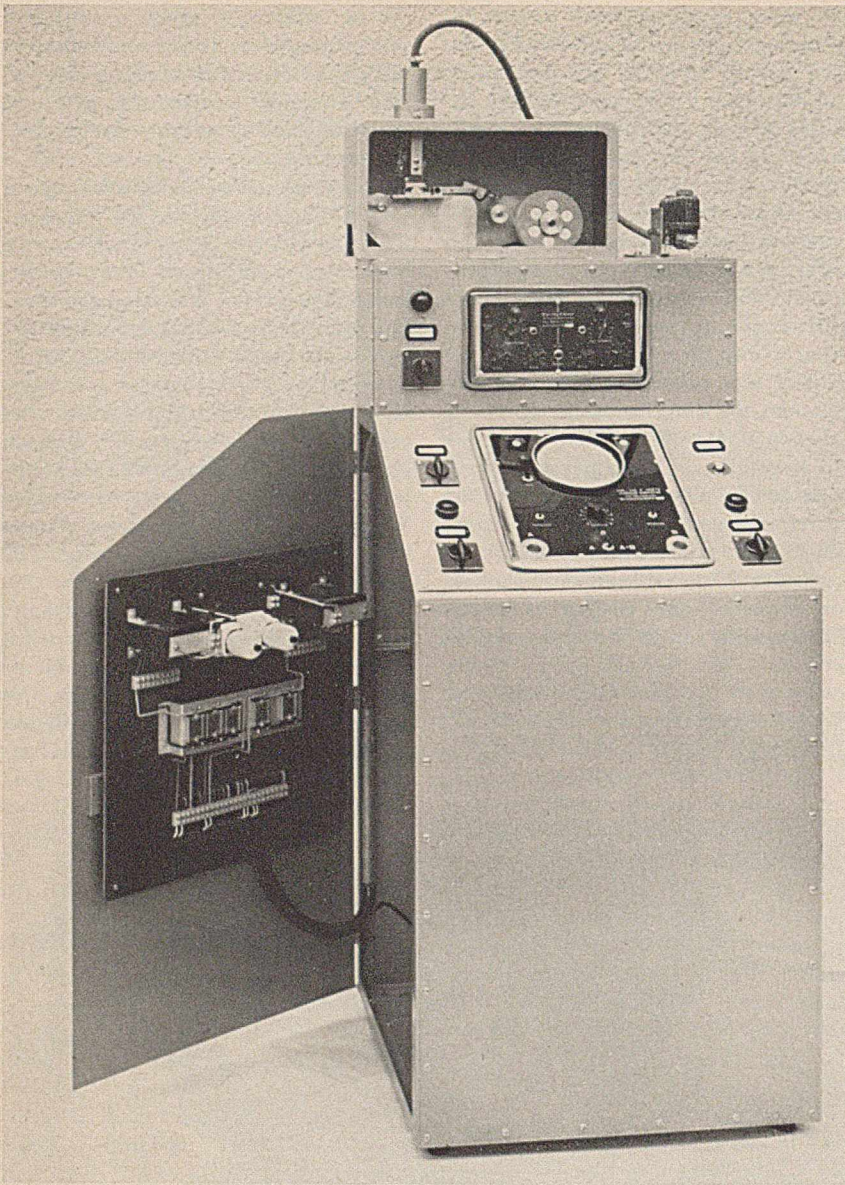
Schaltschrank für die betriebsmäßige Ausführung einer automatischen Prüfanlage für spiralgeschweißte Rohre; Impuls-Schallgerät, Fehlermeldegerät und Schreiber.
